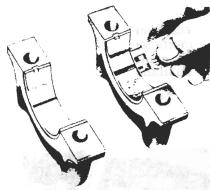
instalação e medição com fio "plastigage" — motor instalado no veículo
